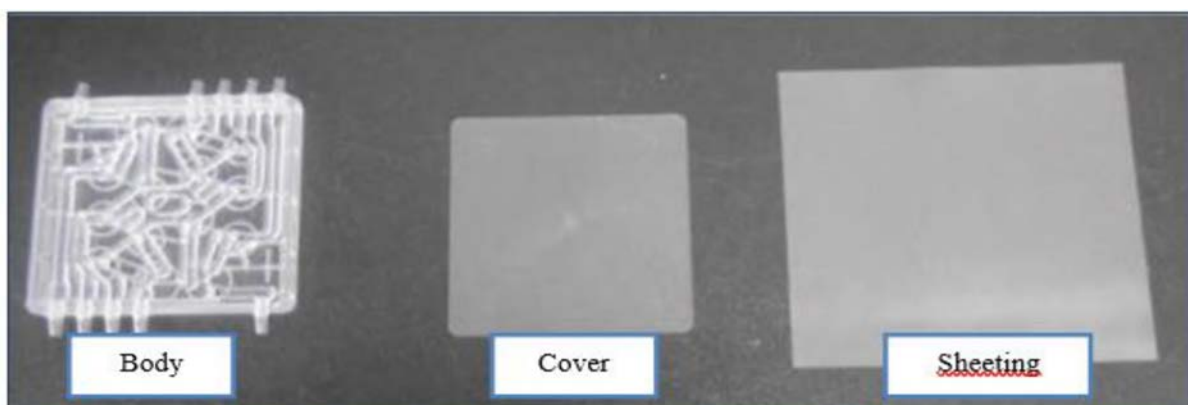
Partes del cassette para la welder. Fuente: propia
